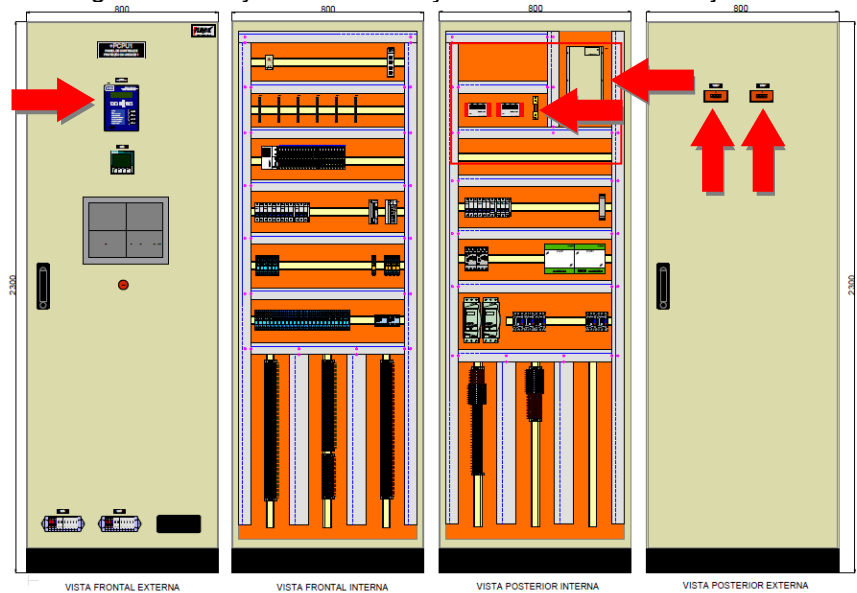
Layout De Fabricação Dos Painéis Do Projeto B.
